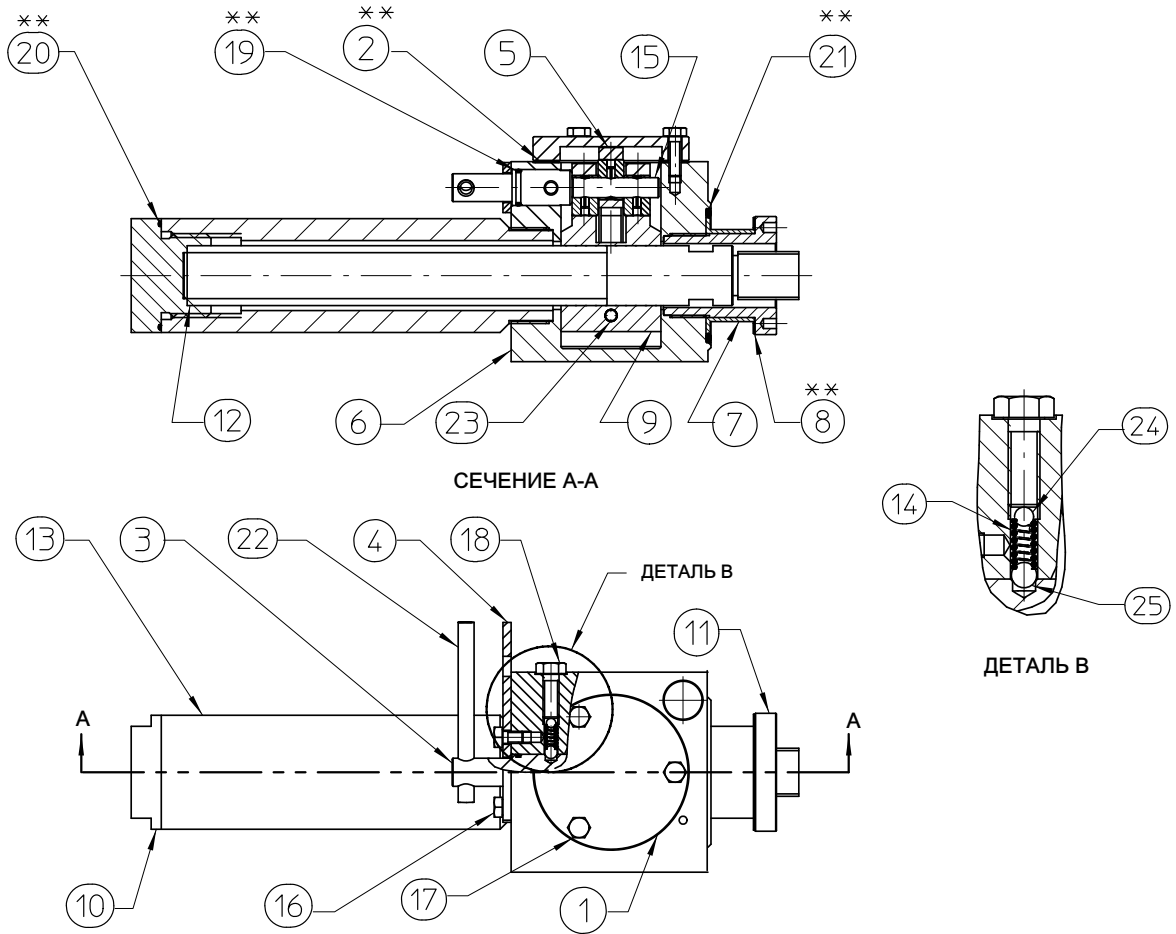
Ручной дублер верхнего монтажа привода Fisher 785С, беспружинный или пружинный возврат, одинарное или двойное действие
